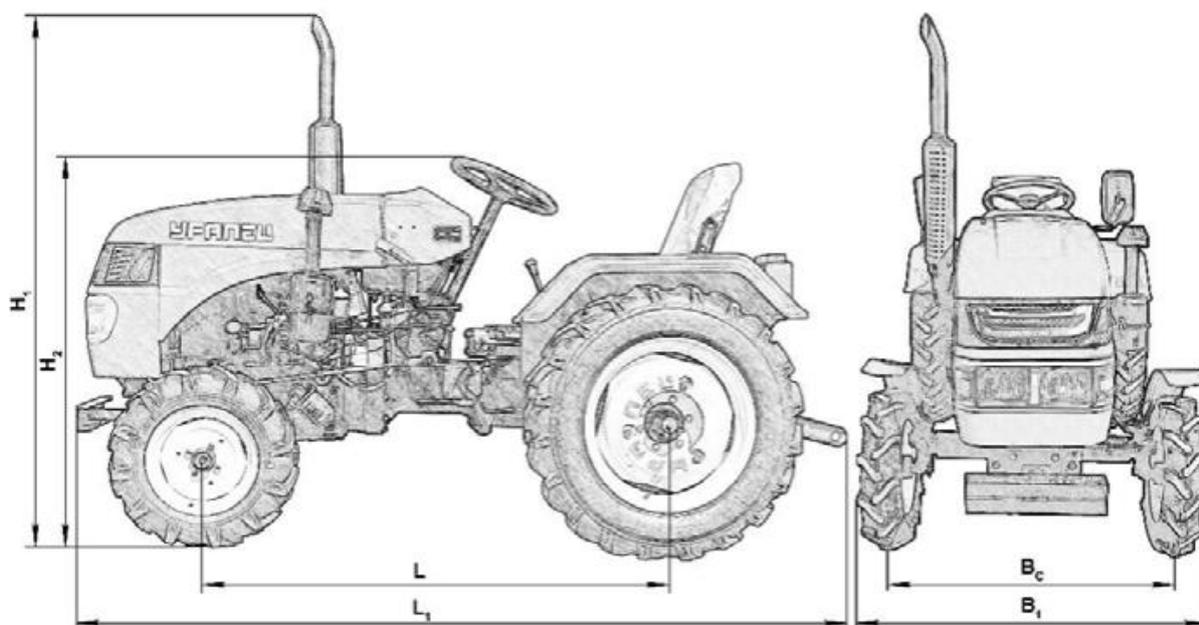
Мини-трактор Уралец-180 с обозначением размеров
